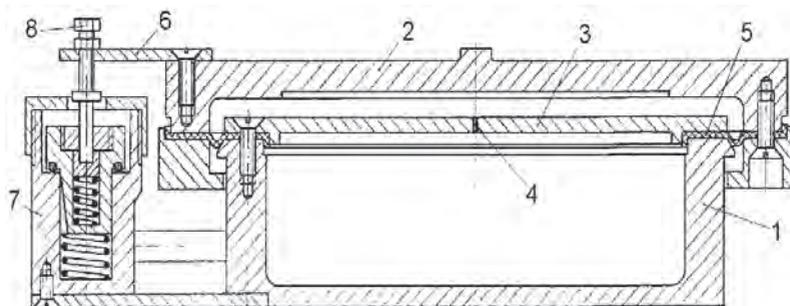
Конструктивная схема пневматической виброизолирующей системы:
